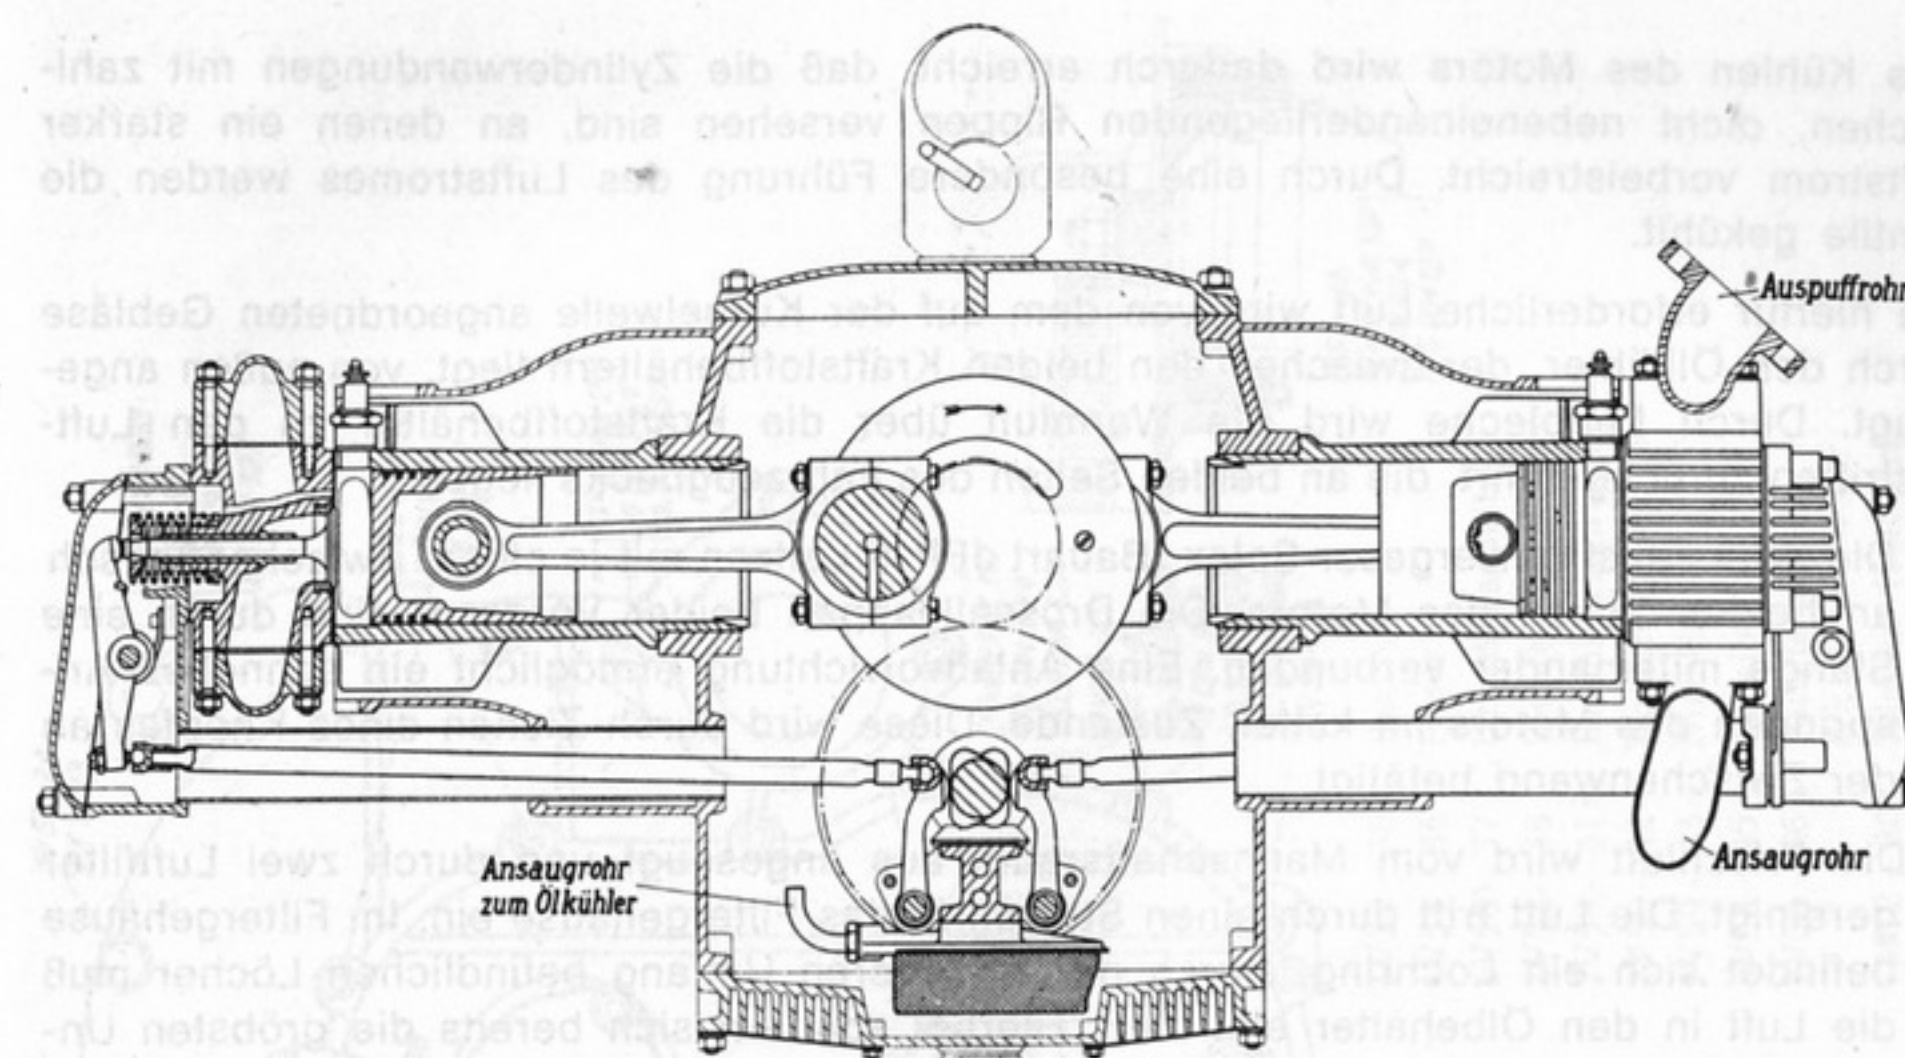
Luftgekühlter 4-Zylinder-Krupp-Motor
